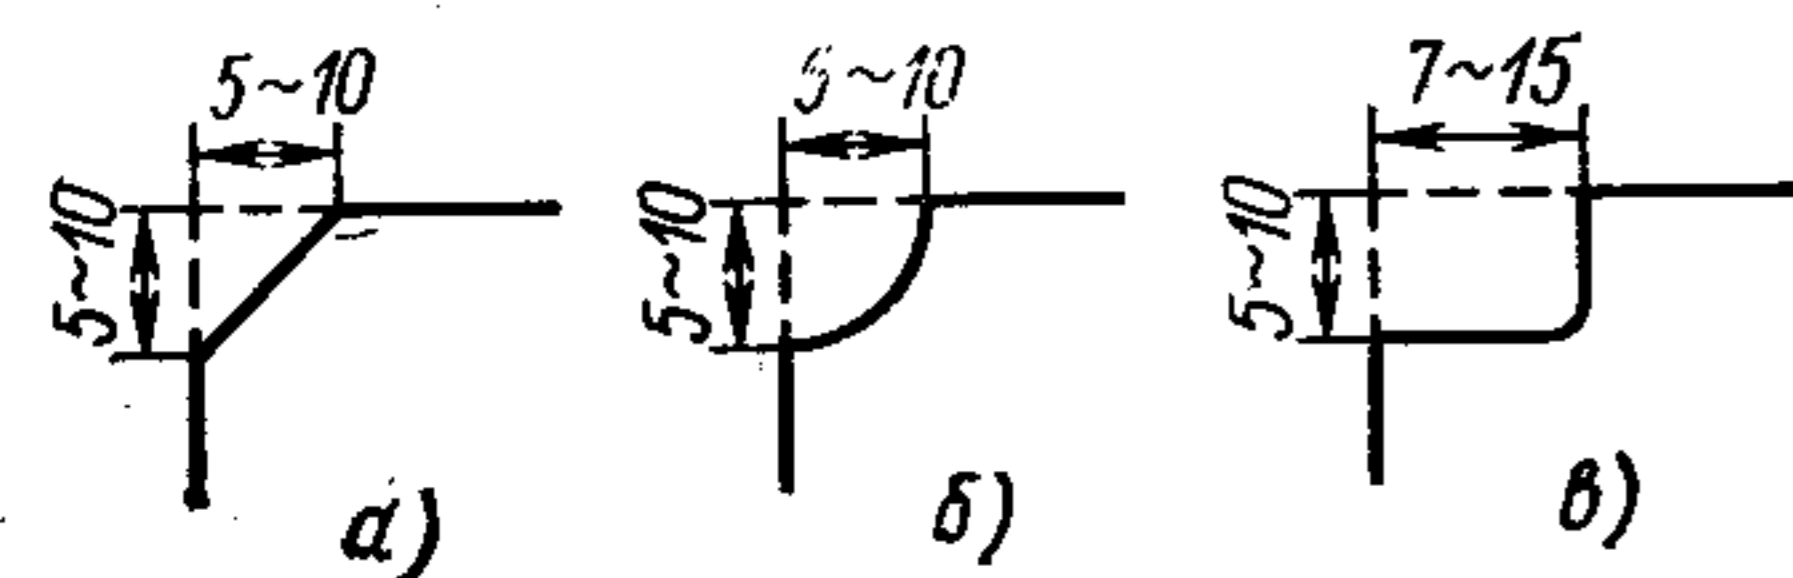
Схема разделки поверхности штампа перед наплавкой
